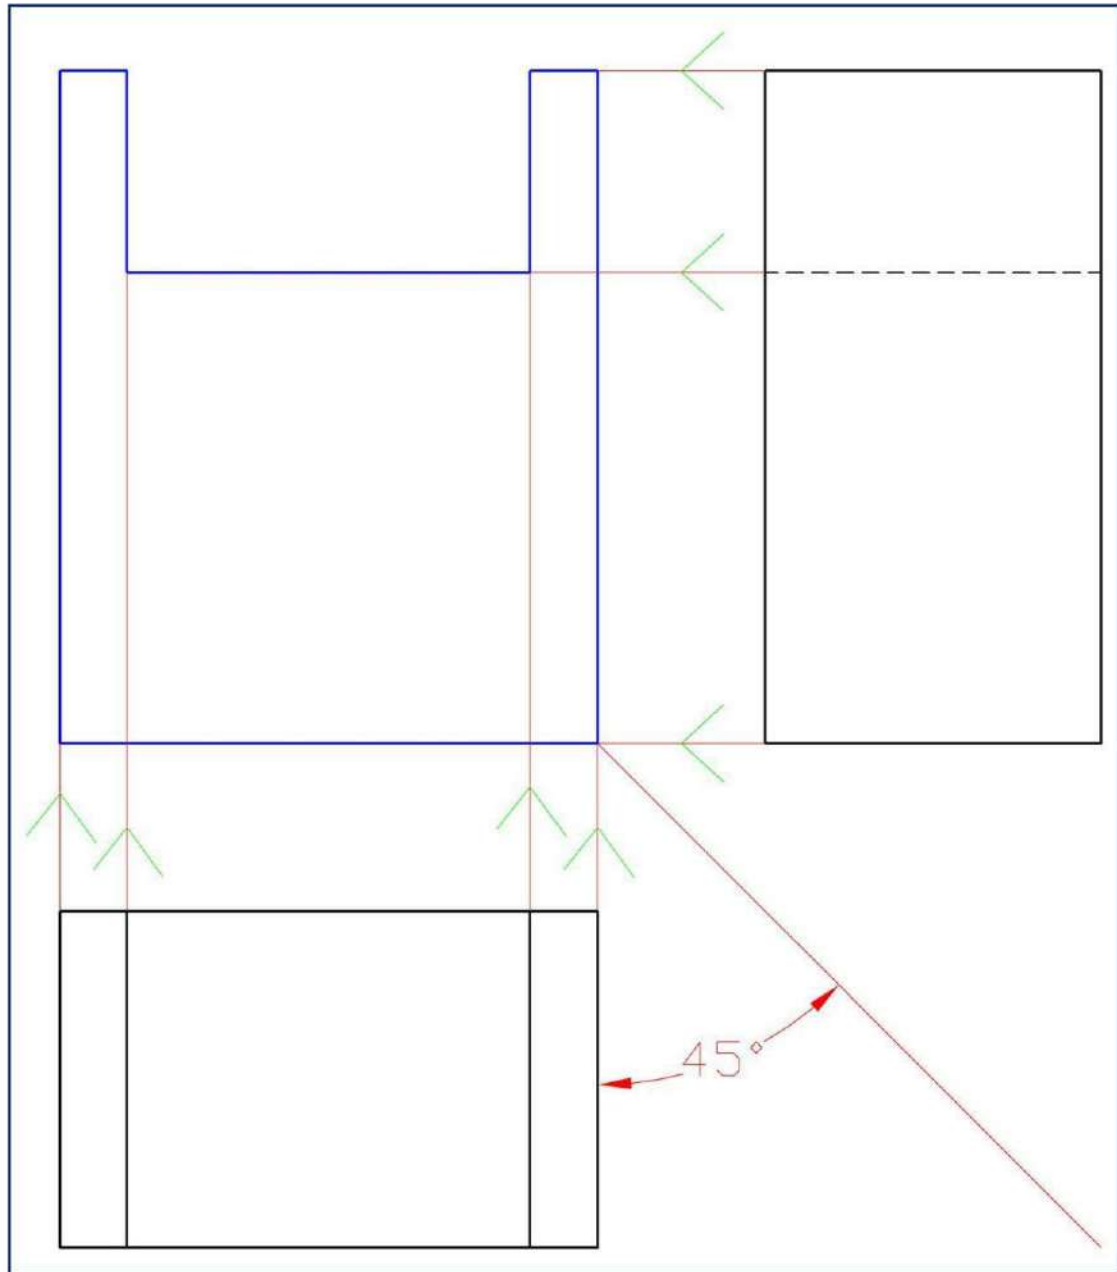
أ المسقط الجانبي والمسقط الأفقي لجسم ما
